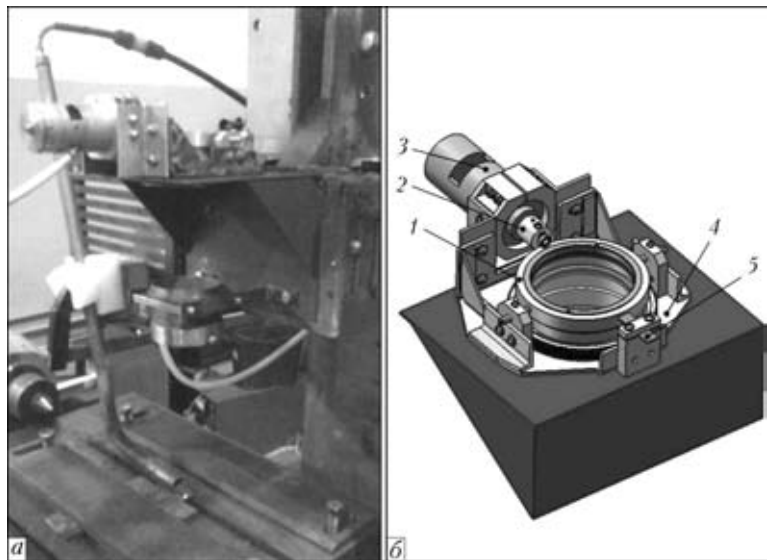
Внешний вид (а) и схема конструкции (б) сканатора лазерного излучения: 1 — обойма с линзой; 2 — эксцентрик; 3 — двигатель постоянного тока; 4 — кронштейн; 5 — пружина
